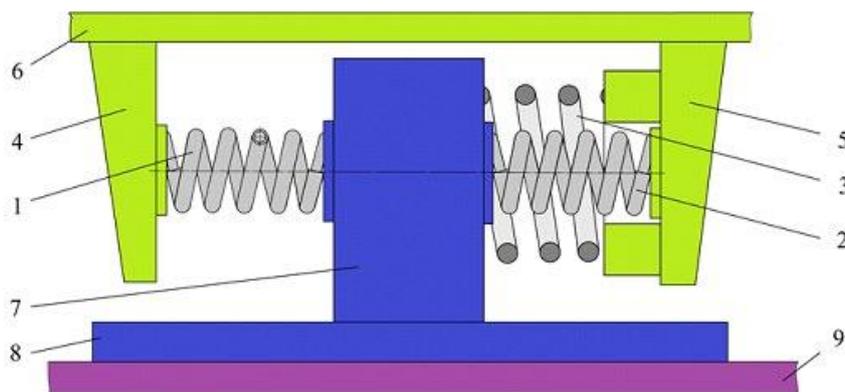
Конструкция билинейной упругой опоры: 1, 2, 3 - стальные пружины; 4, 5 - стойки; 6 - несущий элемент рабочего органа; 7 - стойка; 8 - опора неподвижная; 9 - основание
